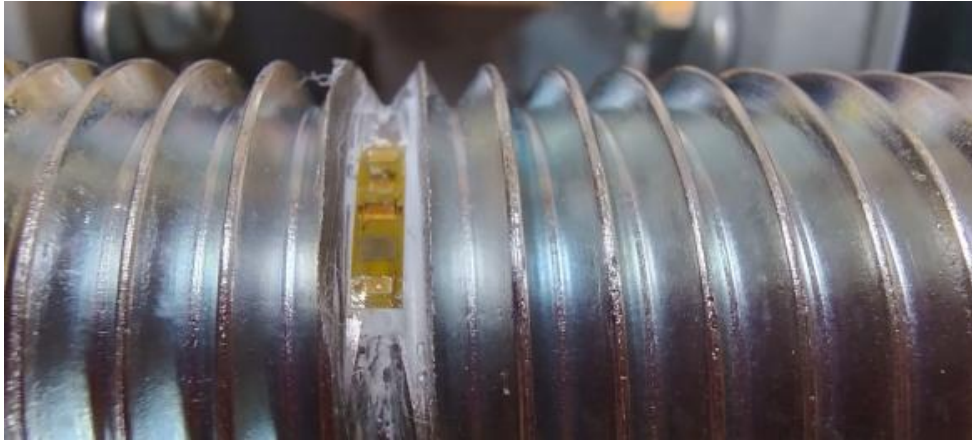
Miniatur-DMS in Gewindegrund einer M30-Schraube.
